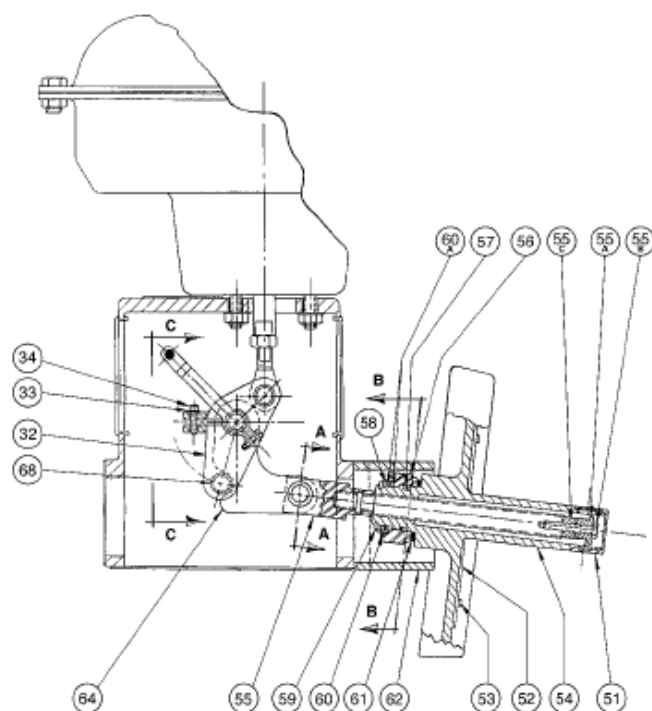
Общий вид маховика. Приводы размера В и С
